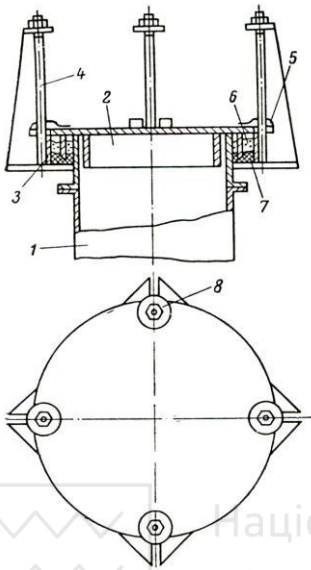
Рухомий запобіжний клапан: 1- труба; 2-клапан; 3-корпус (обичайка); 4- направляюча стійка; 5-пружина; 6-пісок; 7- шлаковата; 8-шайба
